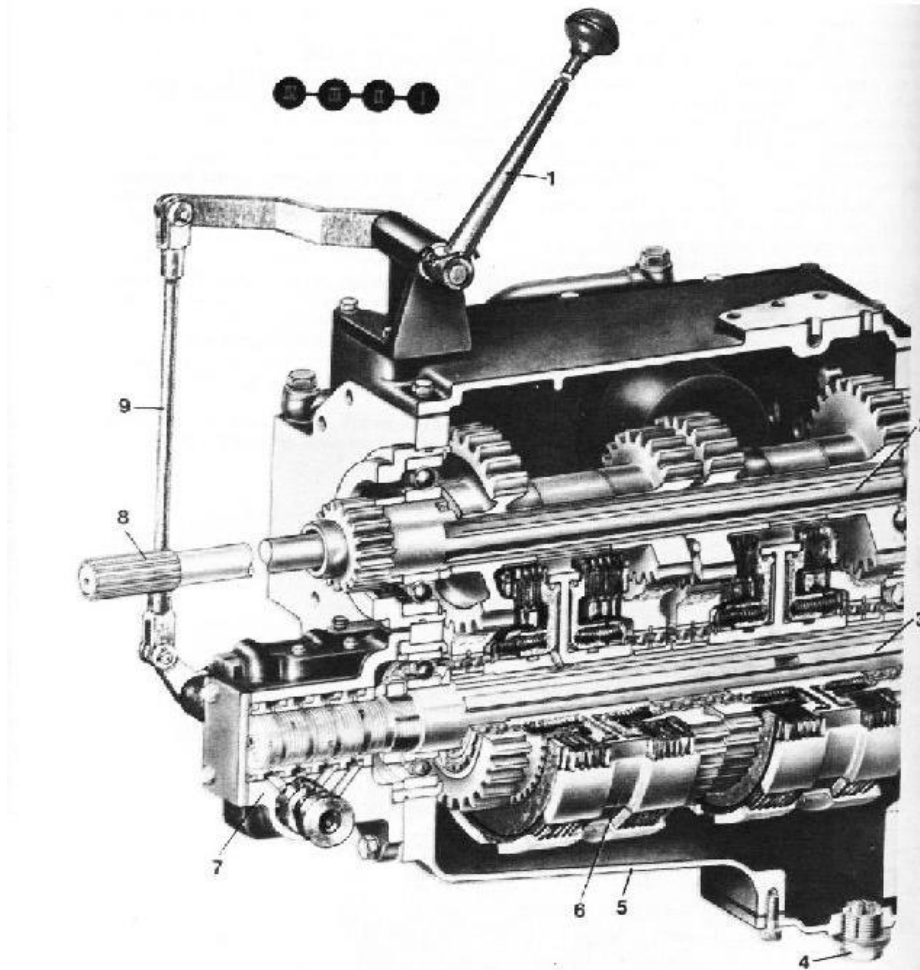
Коробка передач трактора ХТЗ-16131-03.
